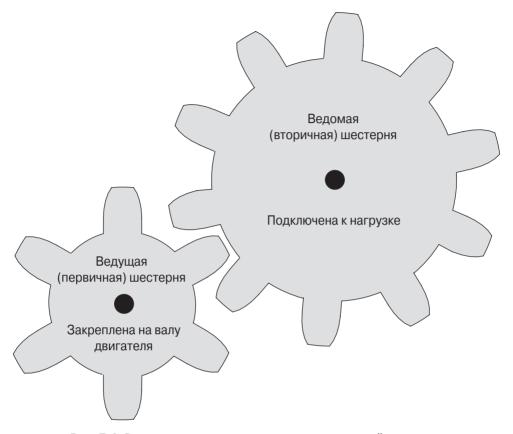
Ведущая и ведомая шестерни механической передачи
